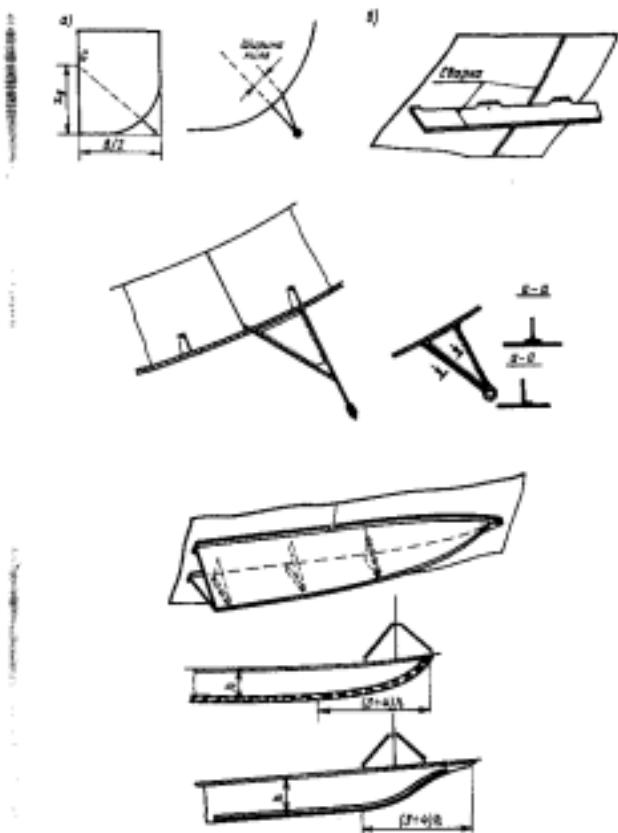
Назначение местоположения точки притыкания к корпусу боковых килей (а) и разницности их конструкций (б)
